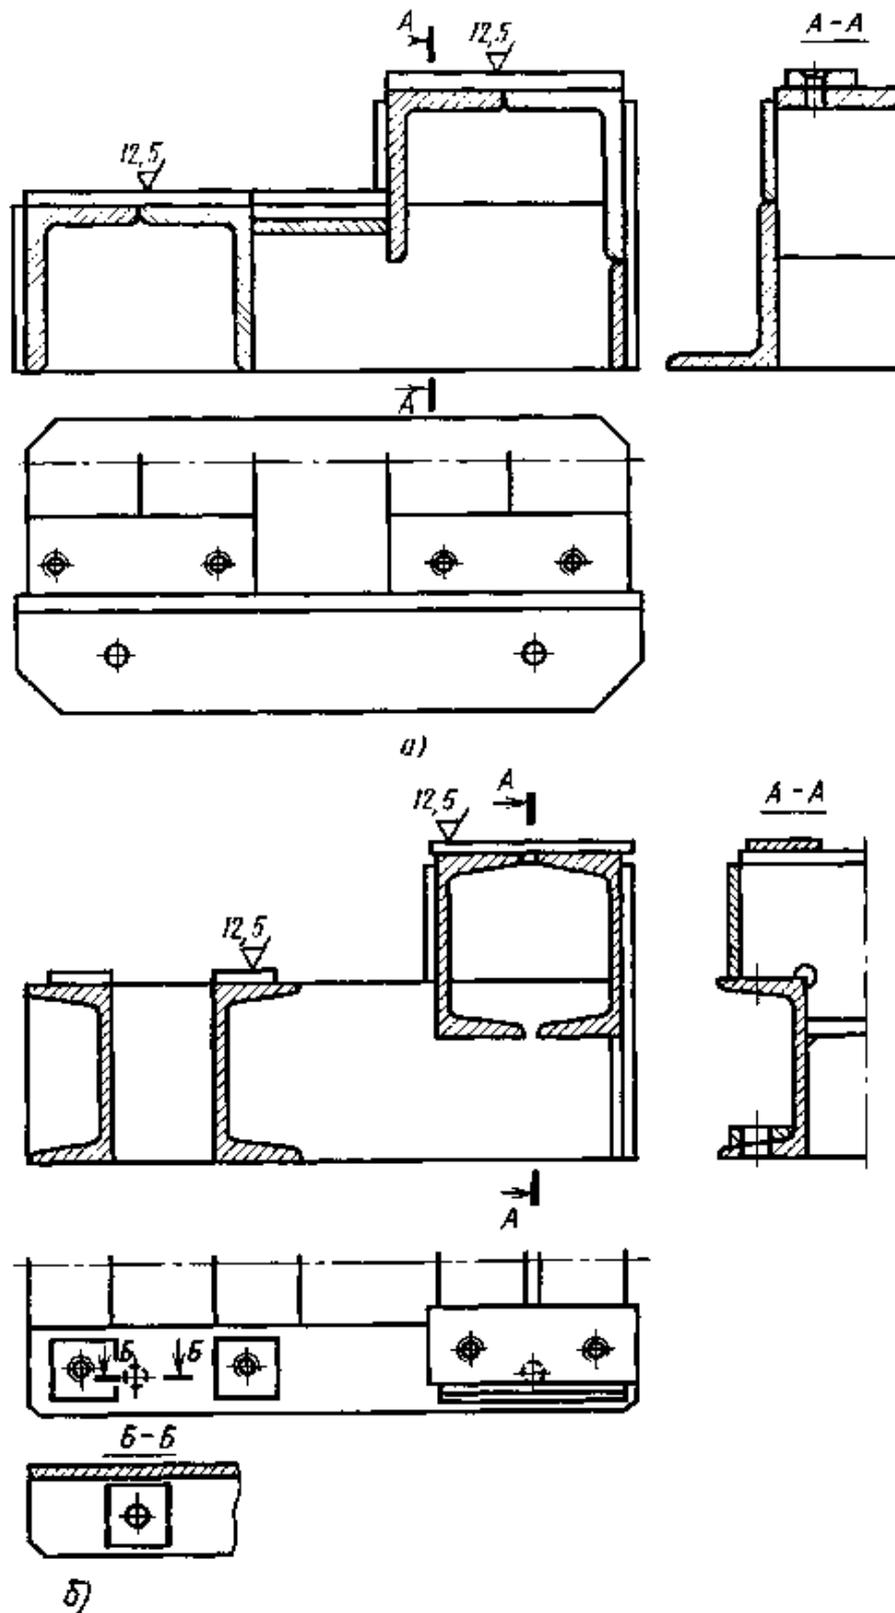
Сварные конструкции плит из уголков и швеллеров
